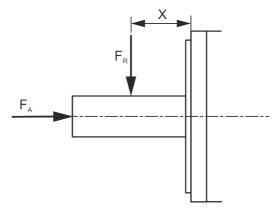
Punto de acción de la fuerza radial F_R y fuerza axial F_A
